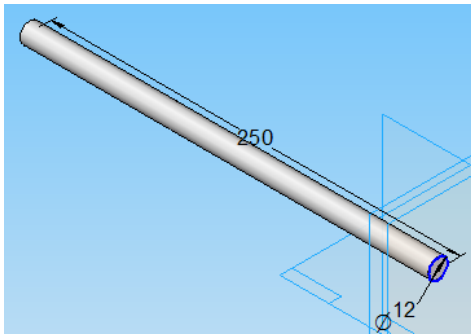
Dimensiones en milímetros de la Barra de apoyo.
